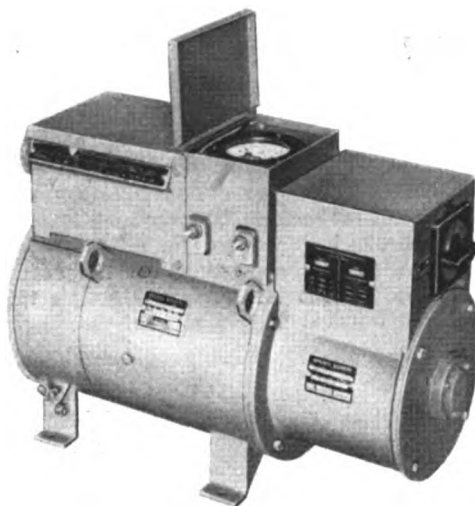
Leichtschweißumformer, Bauart GSAK, Regelbereich 15...200 A. in regengeschützter Ausführung.
